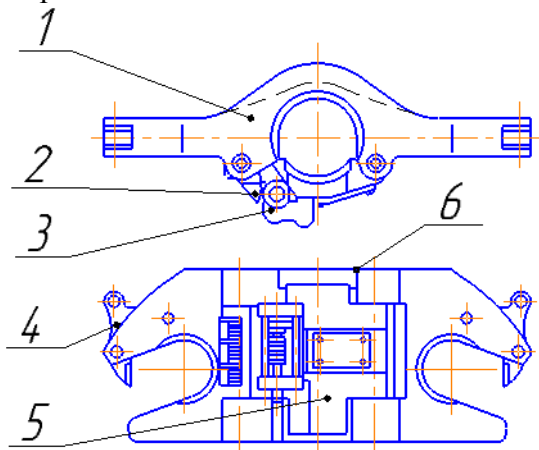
Базова конструкція елеватора: 1 – корпус; 2 – замок; 3 – рукоятка; 4 – замок штропа; 5 – заціпка, 6 – упор для бурової труби
